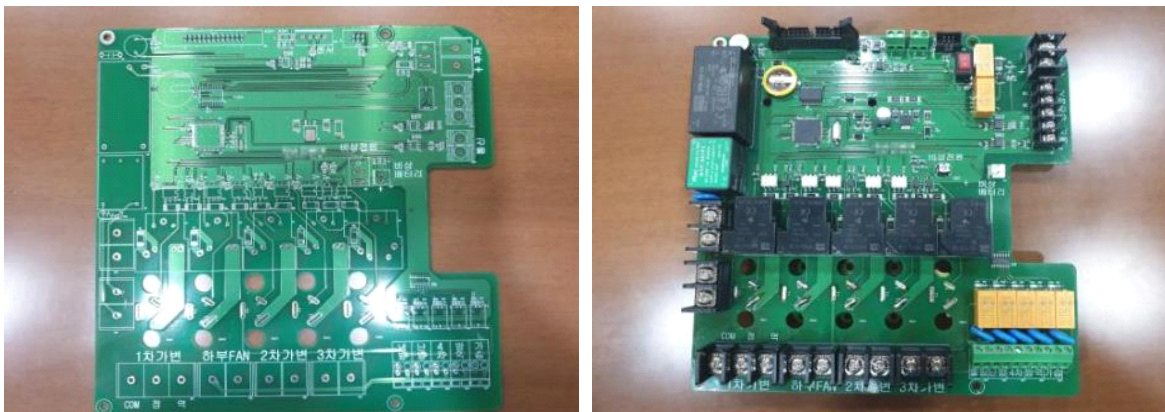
메인보드 PCB 제작 및 SMT 작업 (1)
